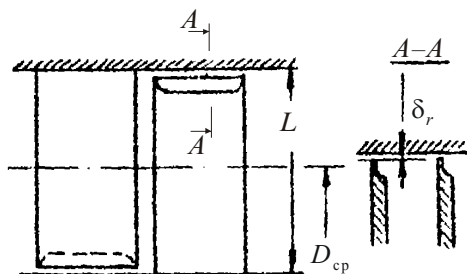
Схема реактивного ступеня з необбандаженими лопатками
